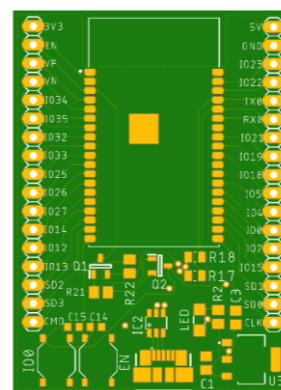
Vista superior PCB (Font: Ernest Porqueras)
